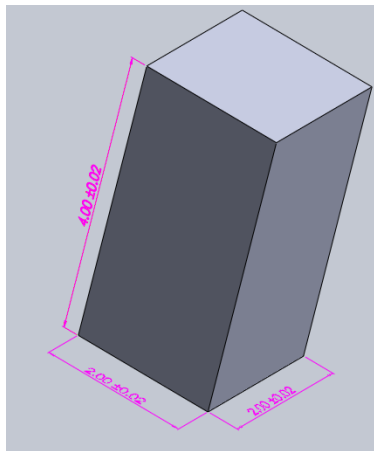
Modelado de la pieza fabricada en la impresora 3D con el material compuesto utilizada para compresión (unidades pulgadas). Fuente: TecNM / ITN.
